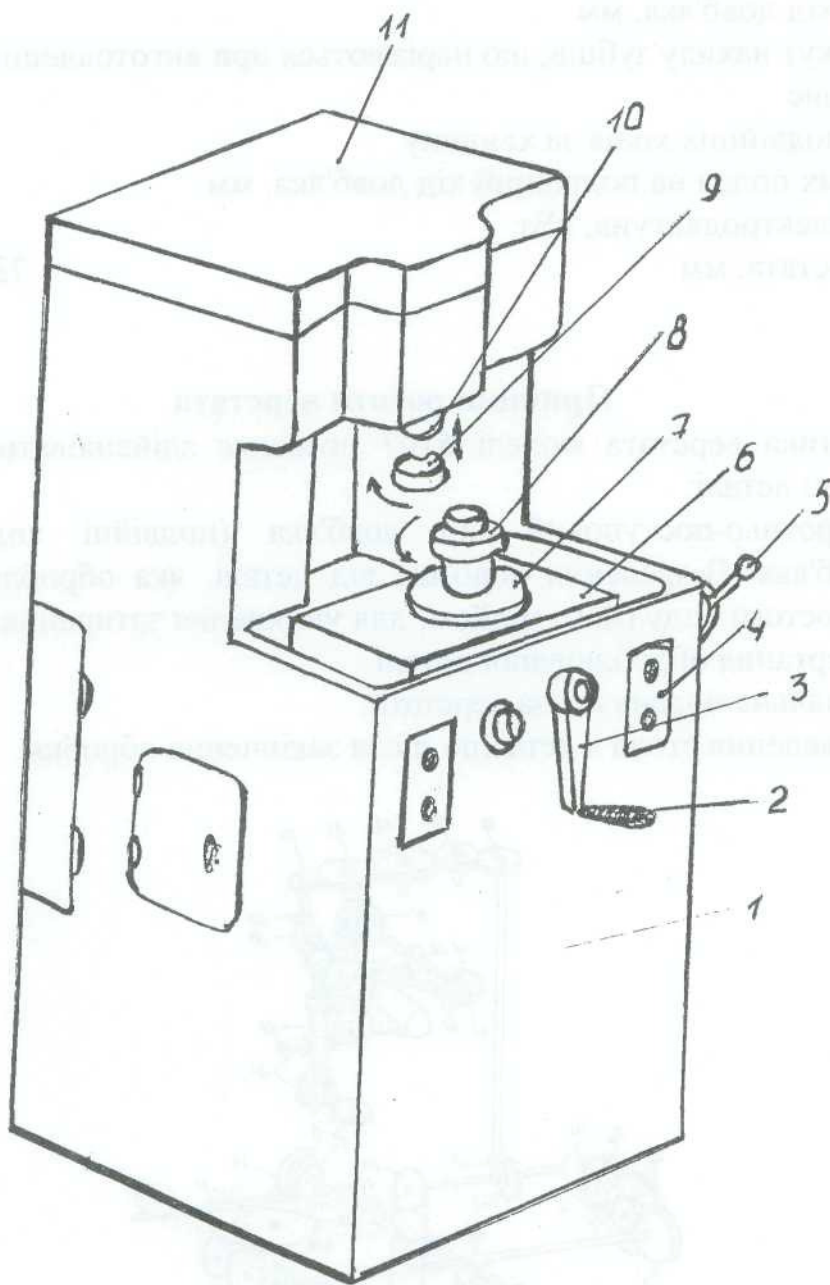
Загальний вигляд зубодовбального верстата:
